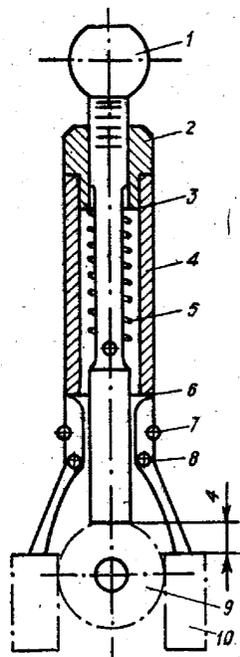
Схемы регулировочных приспособлений положения хвостовика рычага:
